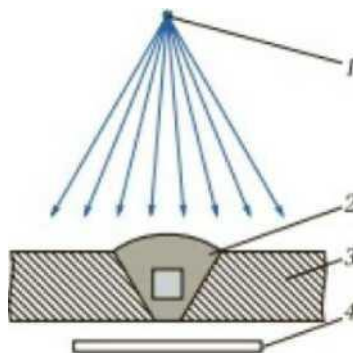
Схема просвечивания сварного соединения
